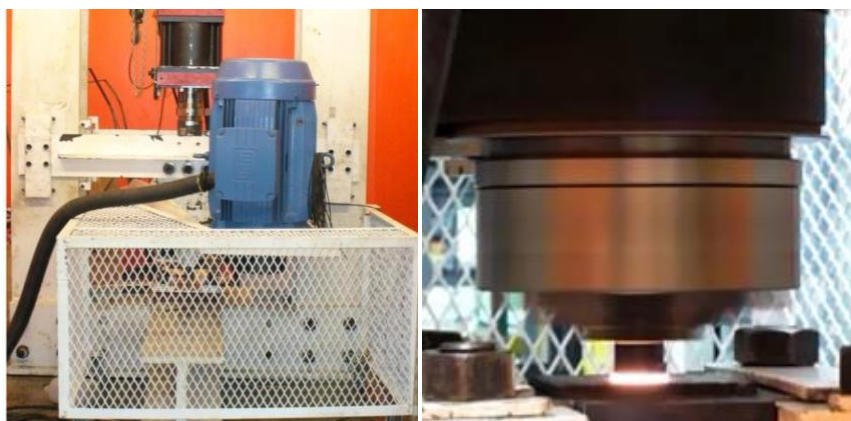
Equipamento de soldagem e solda sendo realizada (MATTEI 2011).
